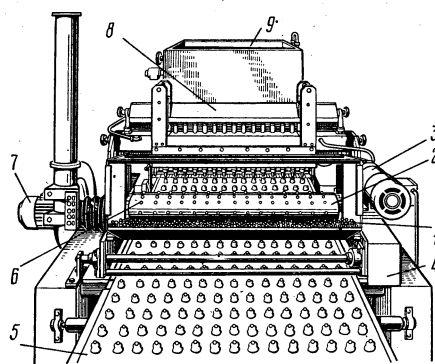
Устройство для механического накладки ядер орехов на поверхность корпусов конфет:
